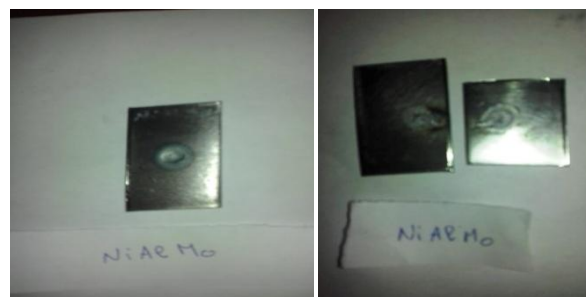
soudage acier /aluminium par poudre NiAlMo.
